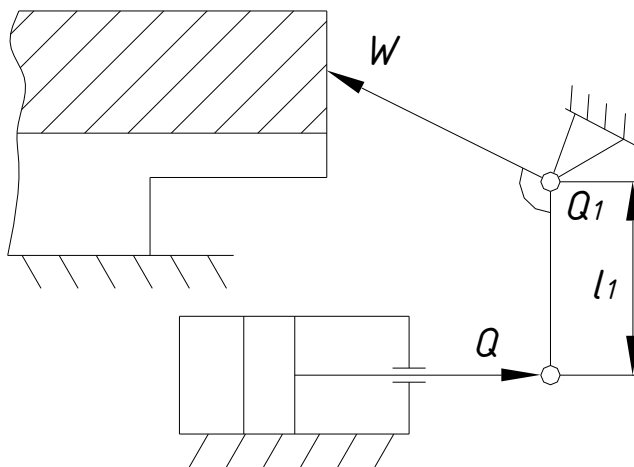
Схема компоновки пристрою. II варіант.
